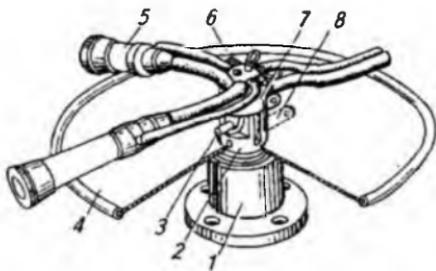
Приспособление для сборки двухтактных доильных аппаратов:
